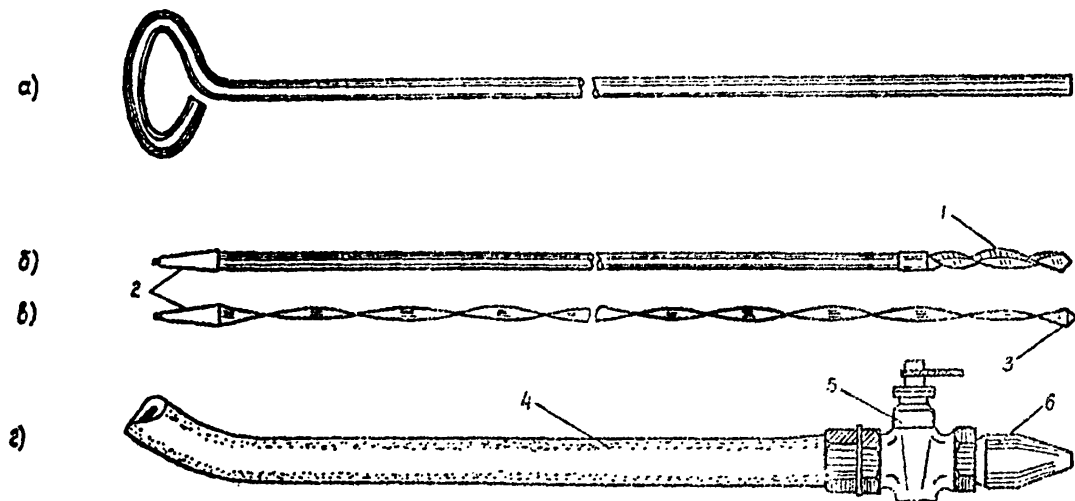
Инструмент для очистки трубок складителей: а - стержень для выталкивания шлама; б, в - стержни для сверления; г - приспособление для промывки трубок. 1 - сверло; 2 - конусы Морзе; 3 - наплавка из твердого сплава; 4 - шланг подвода воды; 5 - пробковый кран; 6 - наконечник
